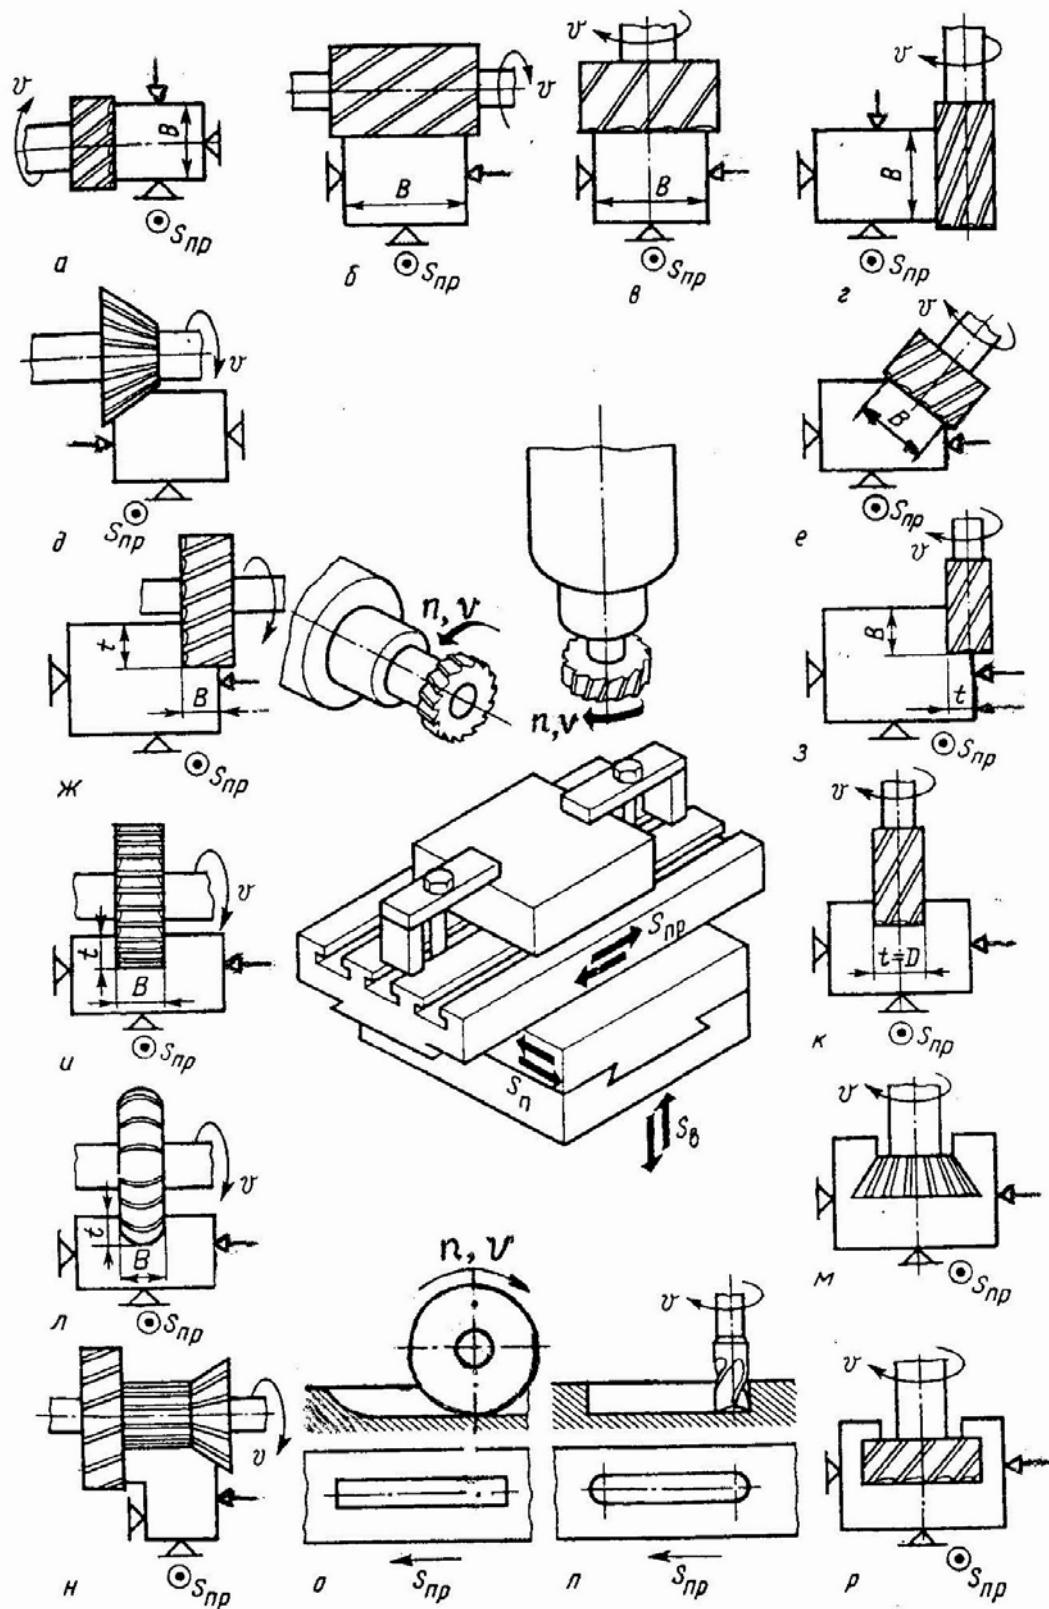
Совмещенные с установкой схемы фрезерования горизонтальным и вертикальным шпинделями широкоуниверсального консольно-фрезерного станка
